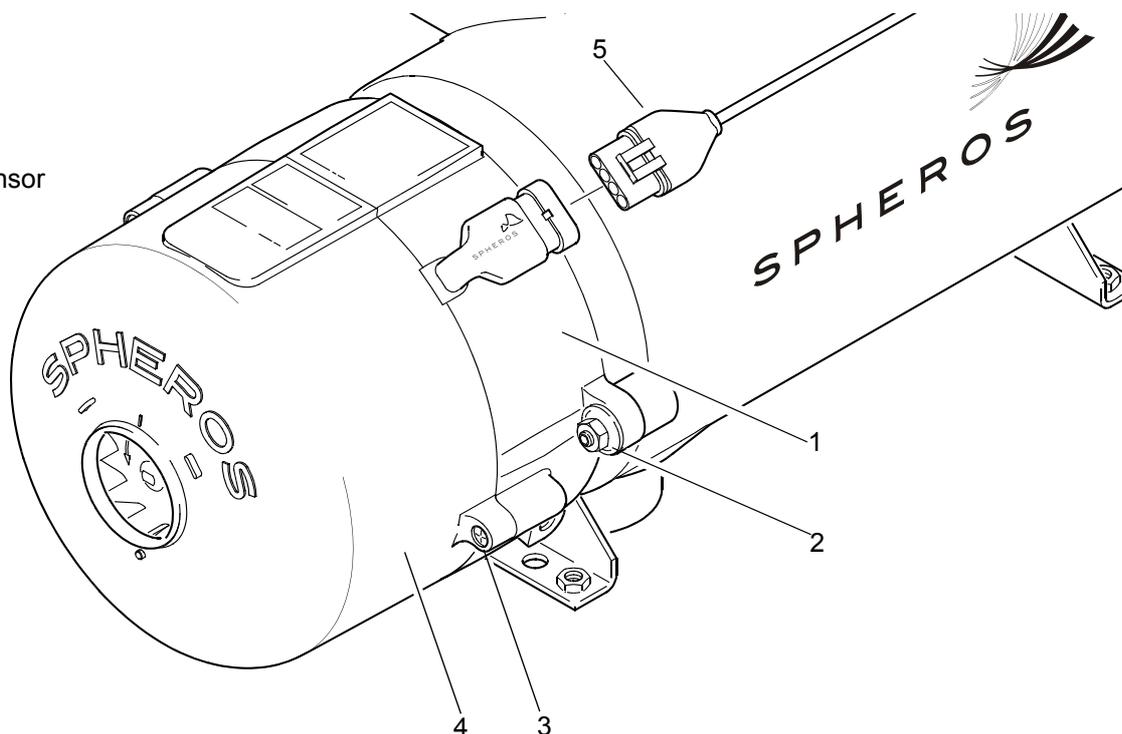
Montaje y desmontaje del cabezal quemador / de la caperuza
